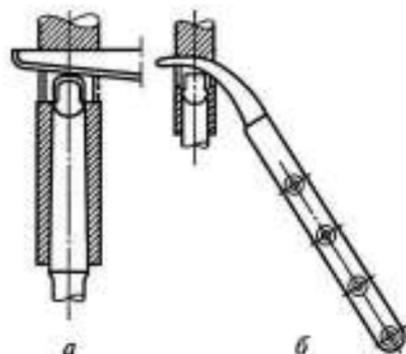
Клинья для удаления инструмента из шпинделя станка:
